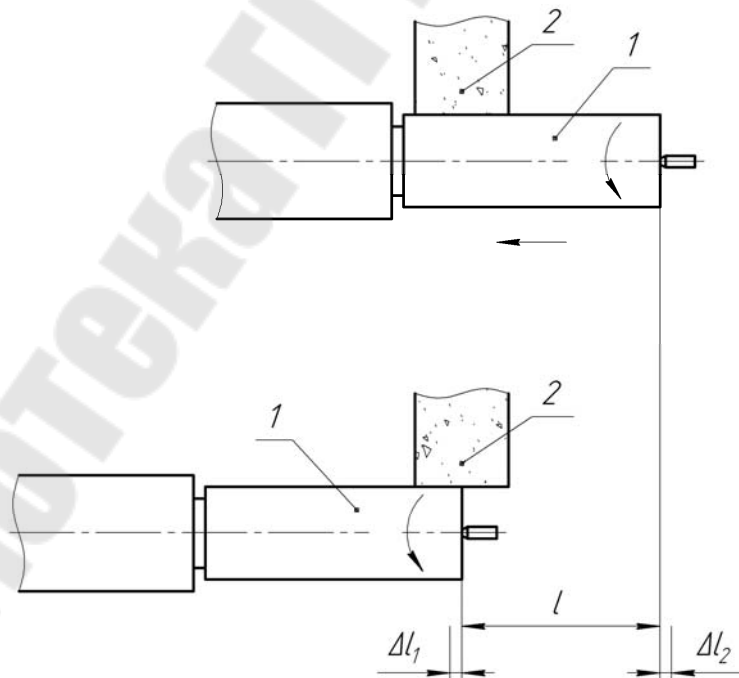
Схема обработки деталей на круглошлифовальном станке
